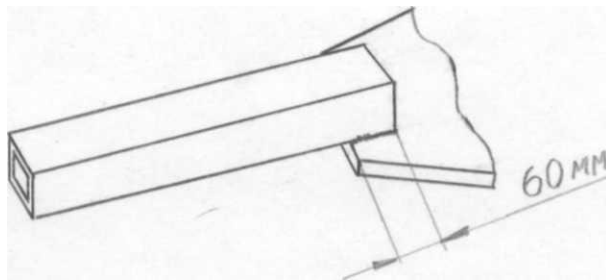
Схема зварного з'єднання тягової труби з поперечною рами
